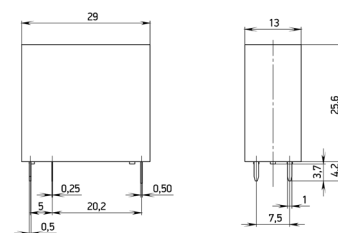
Габаритные, установочные, присоединительные размеры реле OptiRel G RP40-52 и OptiRel G RP40-61 с NO контактами
